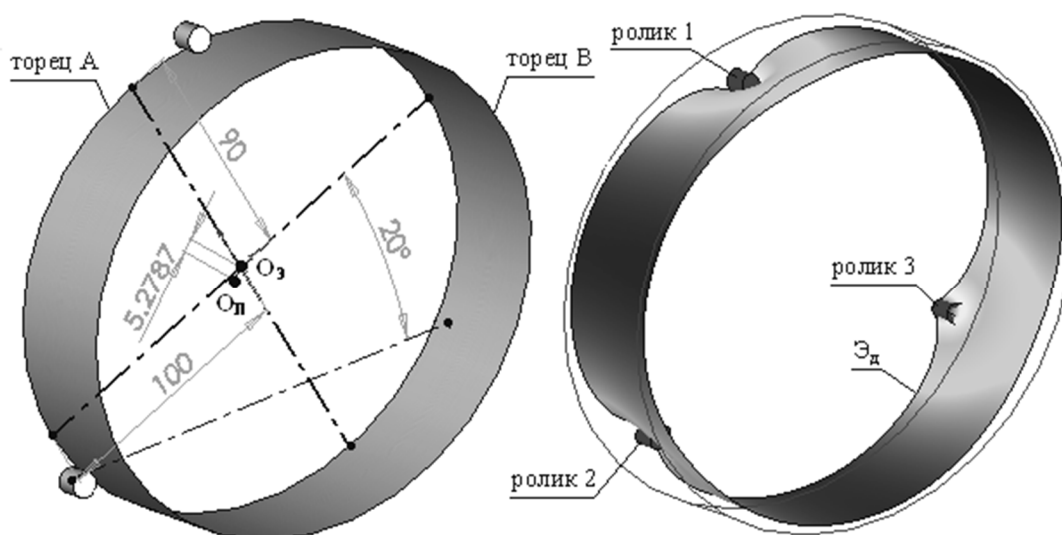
Модель закрепления заготовки в приспособлении с тремя роликами
